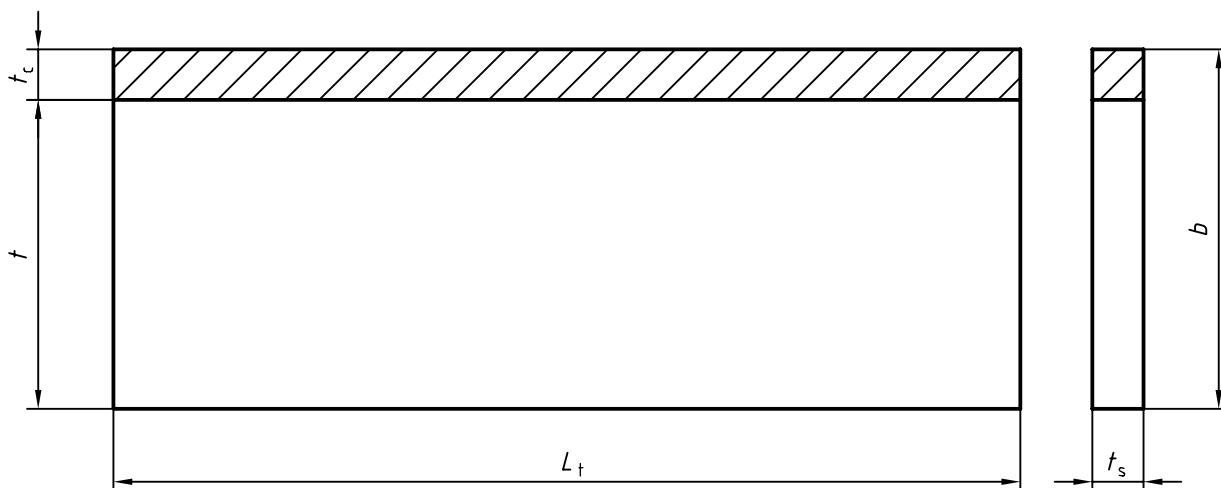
Éprouvette de pliage de côté sur revêtement sans soudure bout à bout (SBC)
